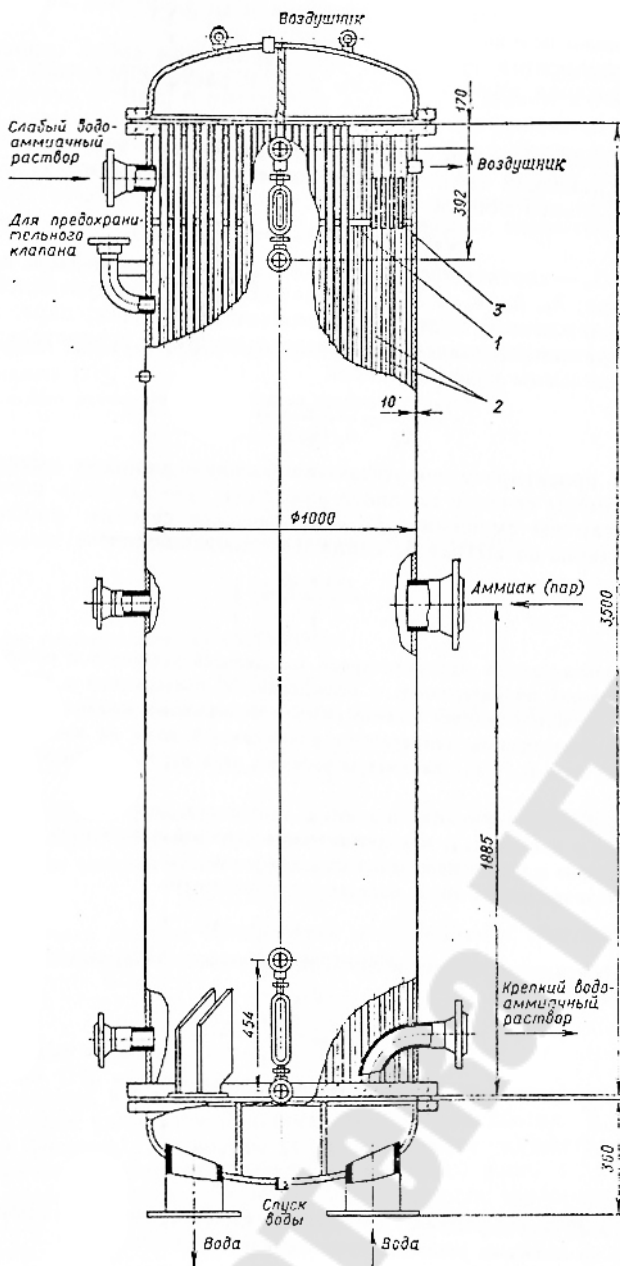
Вертикальный кожухотрубный абсорбер
